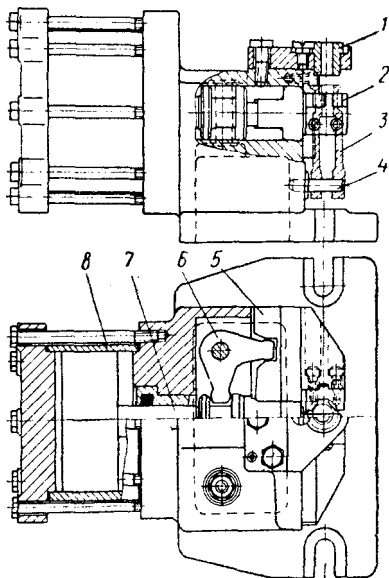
Приспособление с пневмоприводом для обработки отверстий в стяжках и вилках
